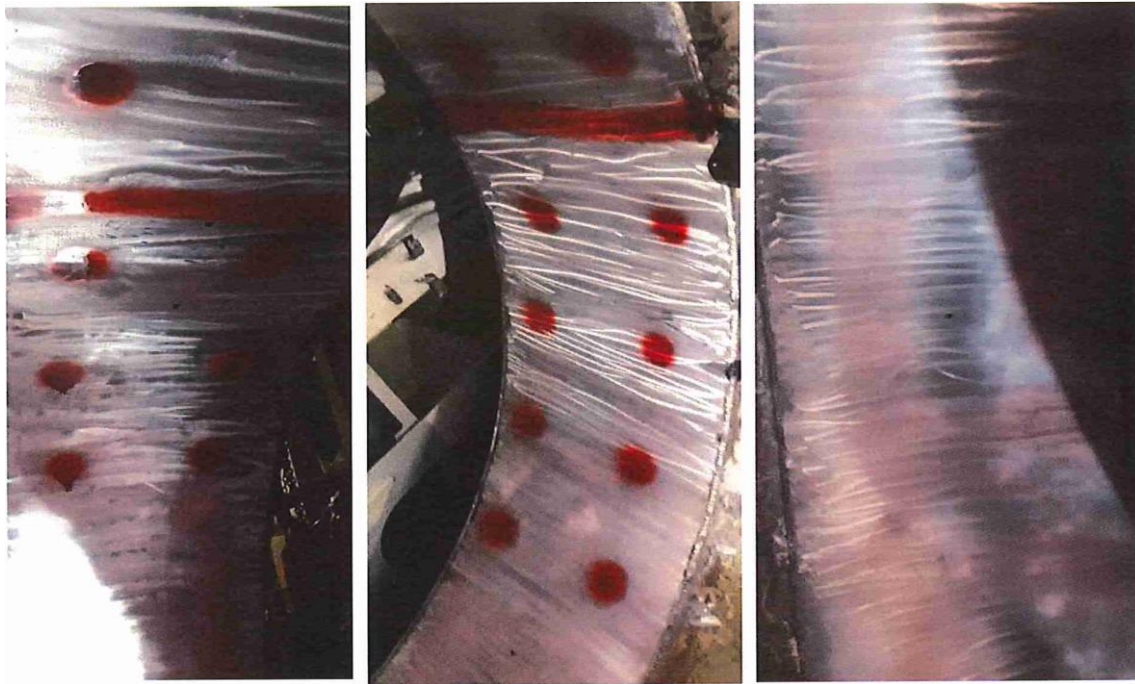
Foto del abotonado soldado en la instalación de la banda de acero inoxidable 316L.
